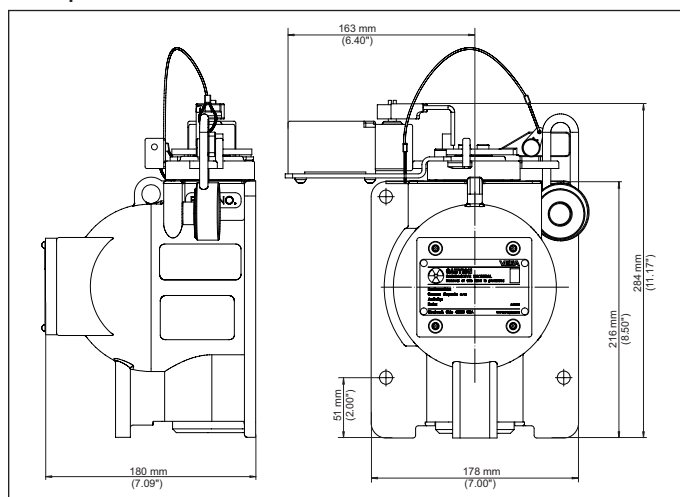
Защитный держатель источника SHLD1, исполнение с позиционными выключателями
